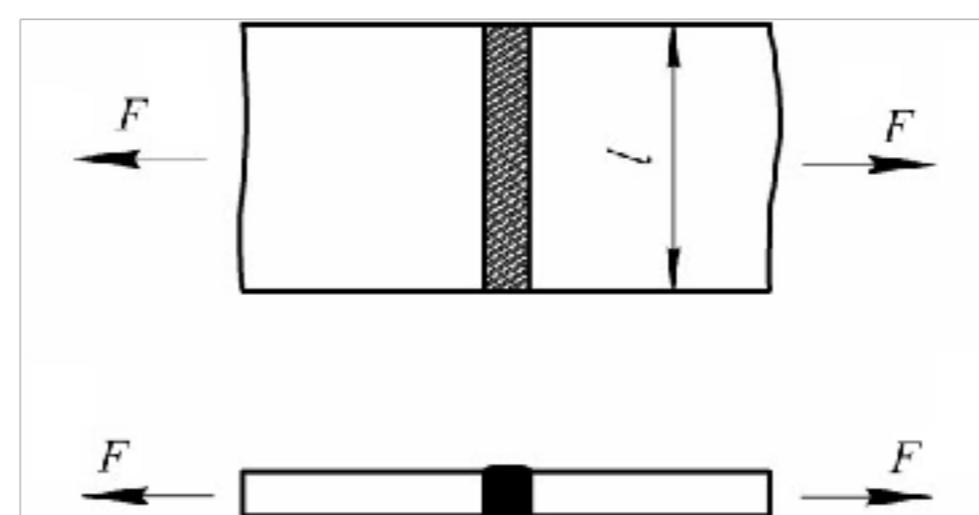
Расчетная схема сварного соединения встык
